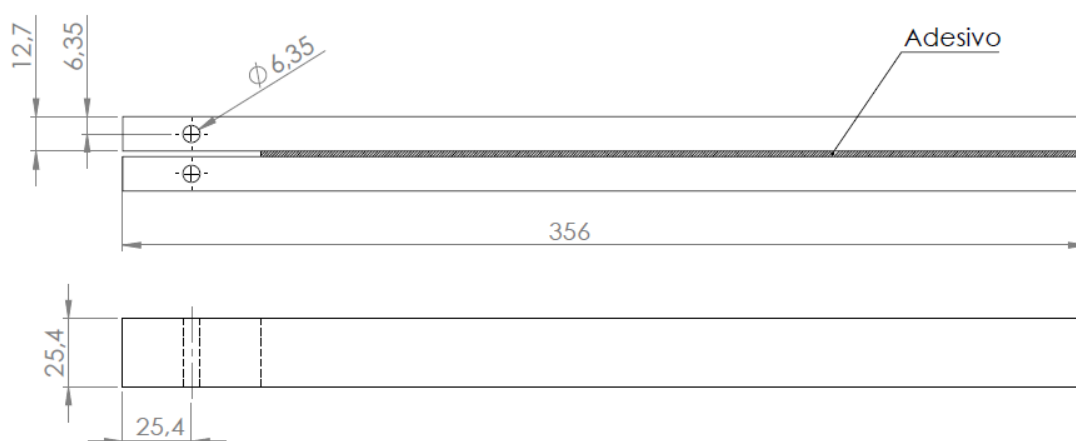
Geometria do substrato DCB (dimensões em mm)
